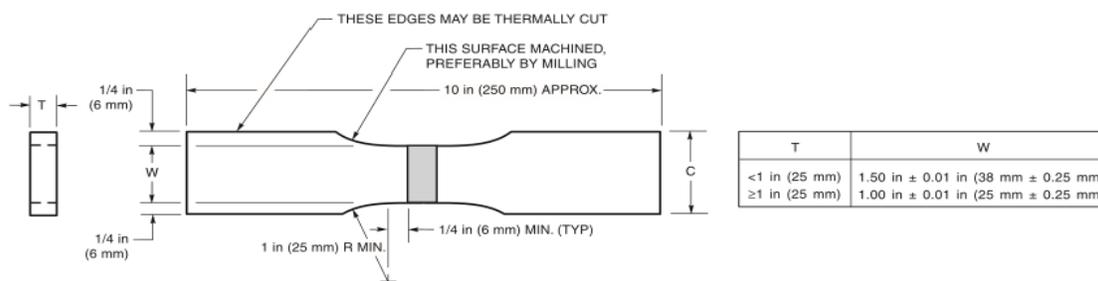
Especificaciones de las dimensiones de la probeta sometida a prueba de tensión por la American Welding Society (AWS), (Society, 2000).
